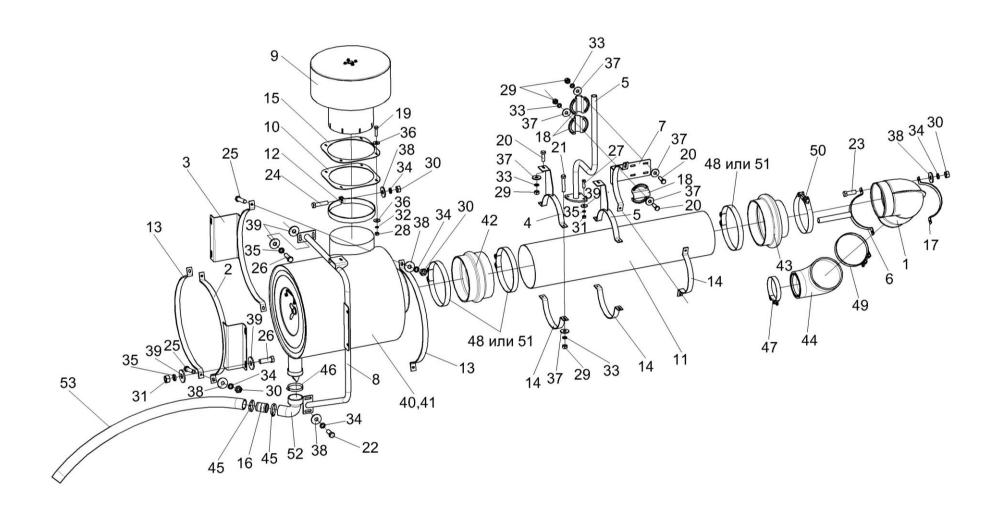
Установка воздухоочистителя КВК 0153000
